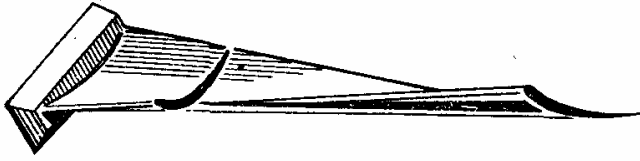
Лопатка компрессора как закрученный стержень переменного сечения
